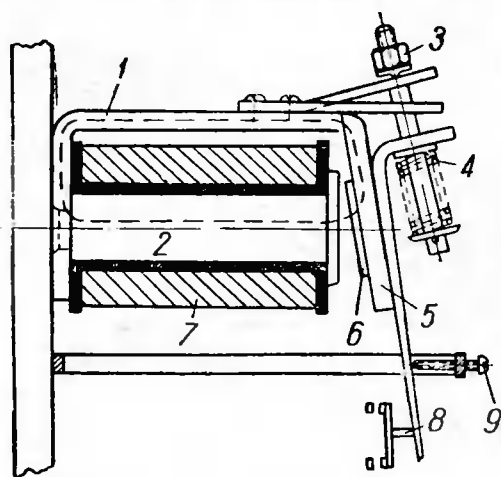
Электромагнитное реле: 1 и 2 — сердечник (наружная и внутренняя часть); 3 — регулировочная гайка; 4 — пружина; 5 — якорь; 6 — немагнитная прокладка; 7 — катушка; 8 — блок-контакт; 9 — упорный винт.
